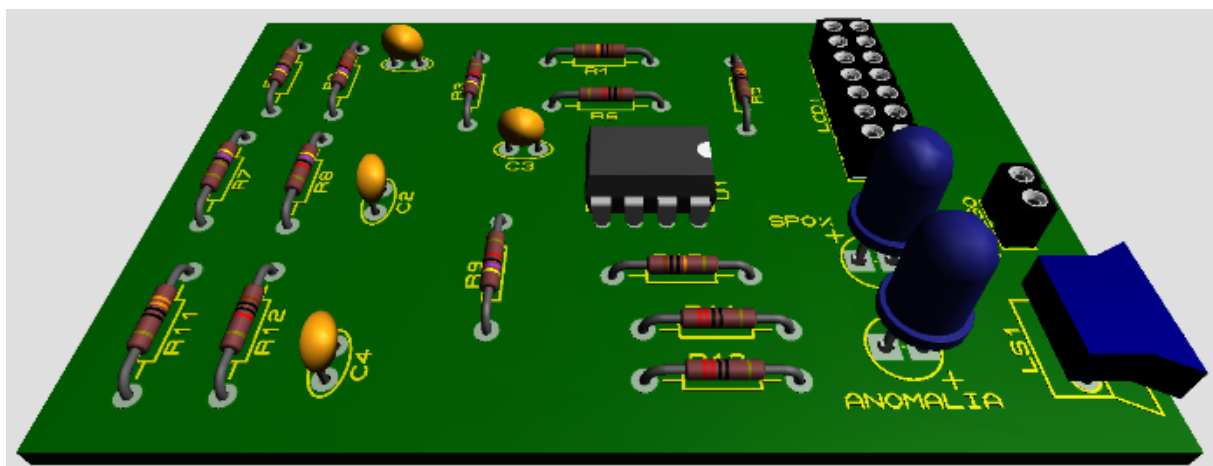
Vista Frontal de Circuito en Placa PCB
